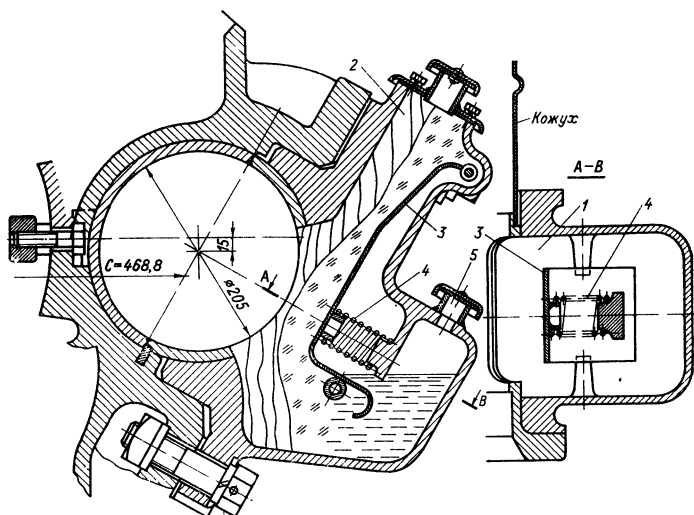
Моторно-осевой подшипник тепловозного тягового двигателя
